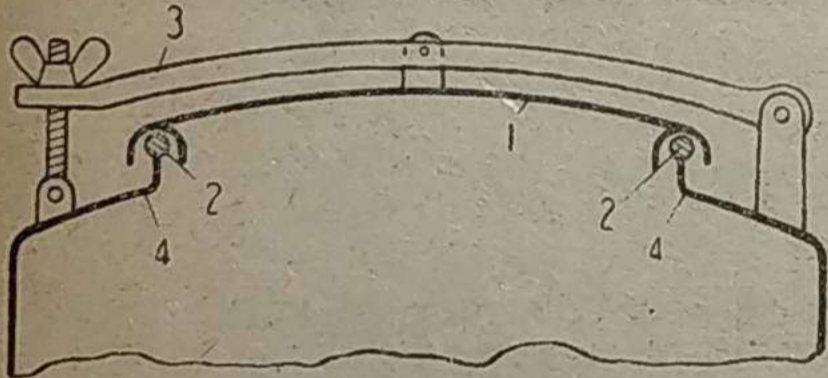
Схема устройства уплотнения крышки загрузочного люка у газогенератора
